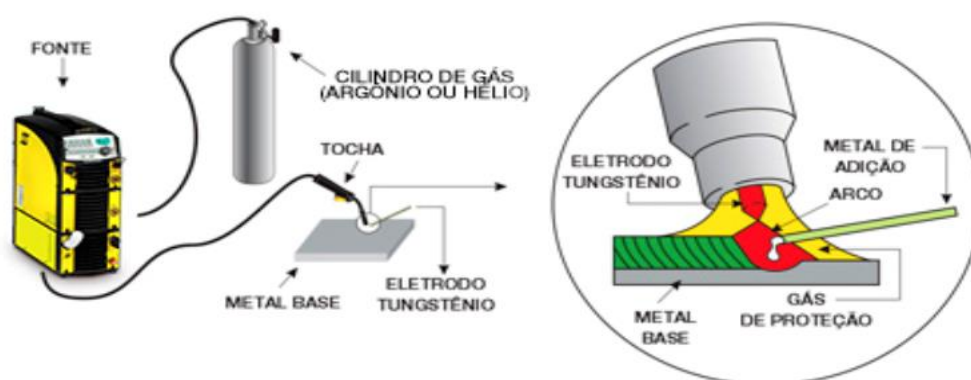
Soldadura por processo TIG (GTAW)
